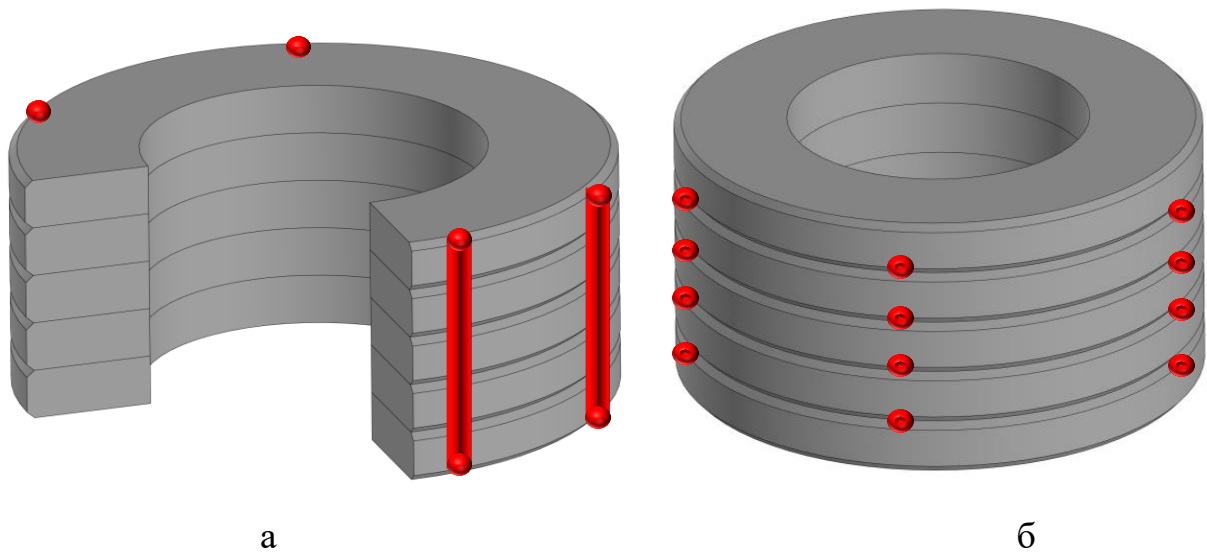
Изготовление переплавляемого электрода: а– путем нанесения сварных швов вдоль образующей цилиндра электрода; б – путем точечной сварки по внешней окружности контакта дисковых ножей
